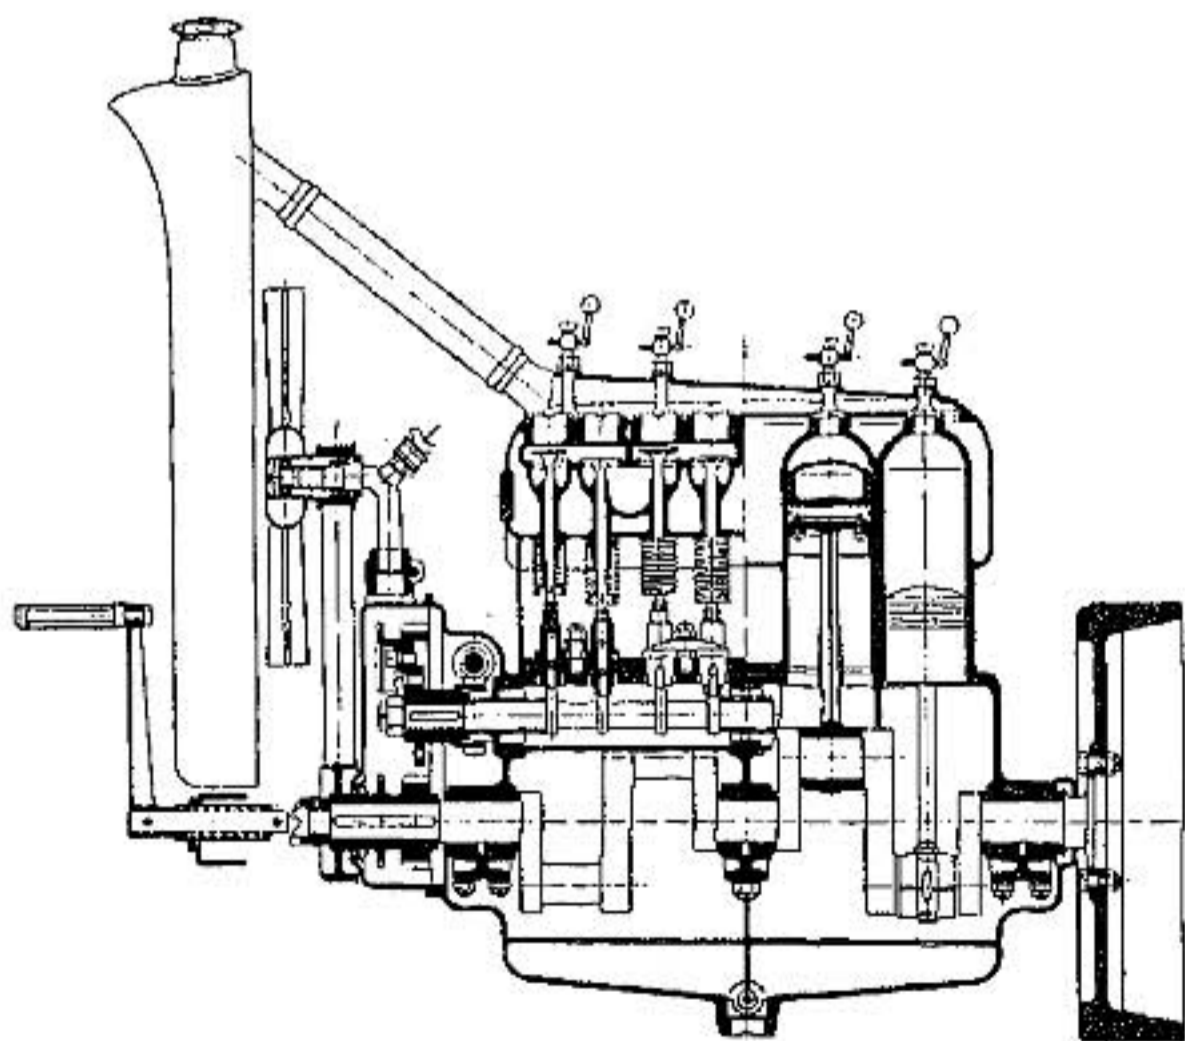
Продольный разрѣзъ двигателя Дессау.
